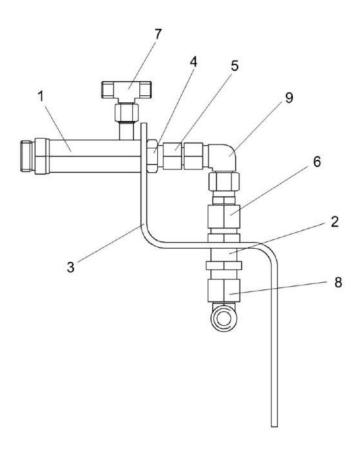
Установка клапана дренажного КВК 0601660 (вид сверху)
